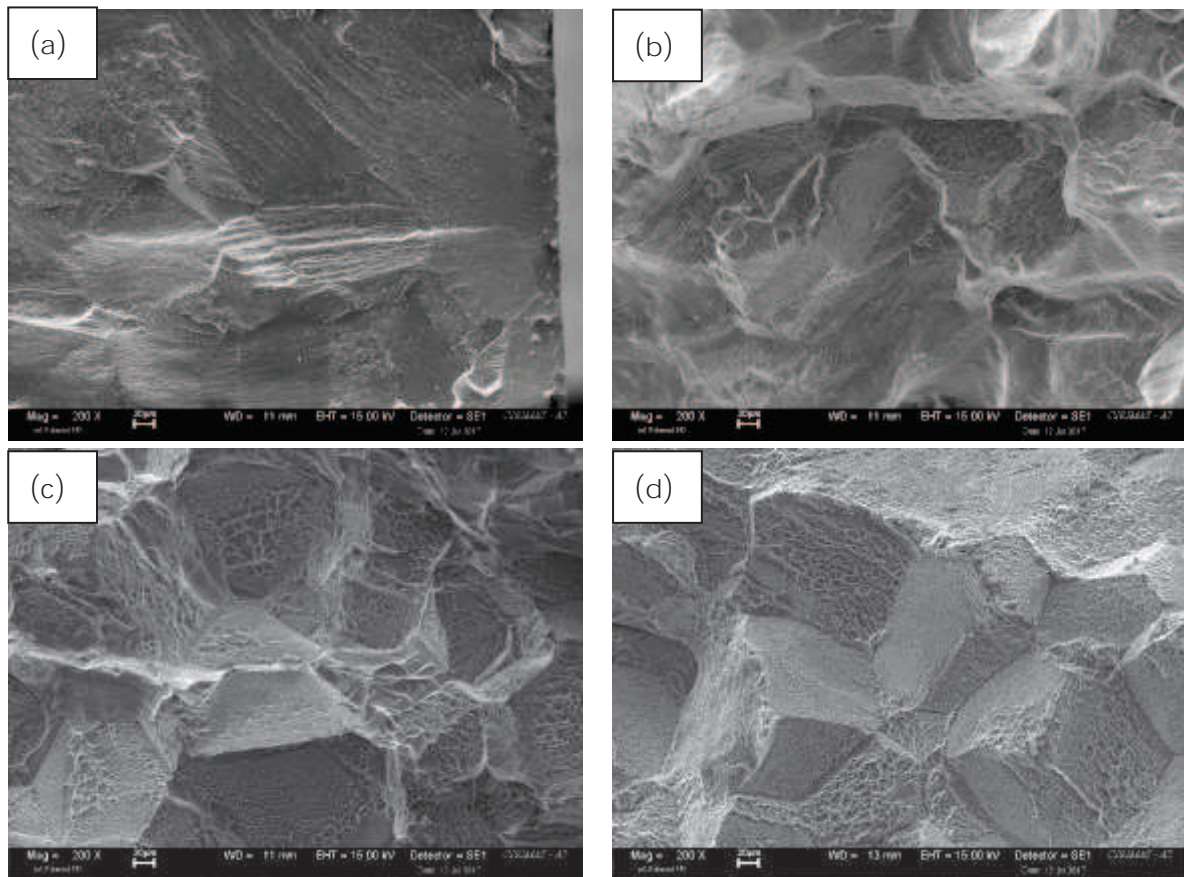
Détails des faciès présentés en Figure V-28 de l'éprouvette non vieillie (a) et des éprouvettes vieilles pendant 500h à 450°C (b et c) et 600°C (d)
